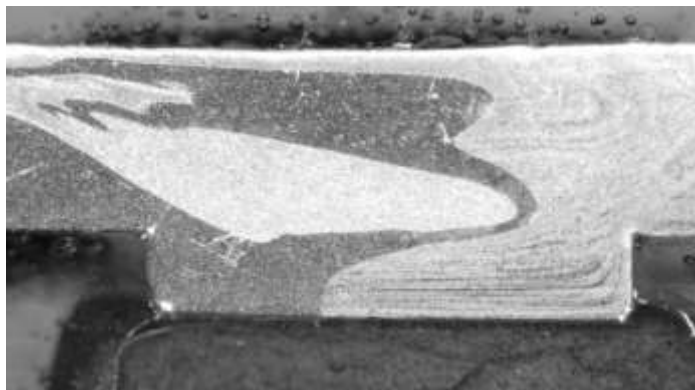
Структура сварного соединения сплавов В-1469 и В-1579
